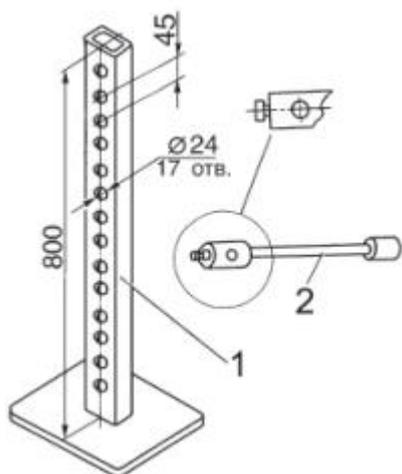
Дополнительная опора для ключа крепления гаек колес:
